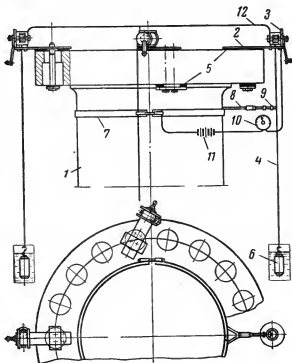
Приспособление для центровки вала турбины по струнам.
